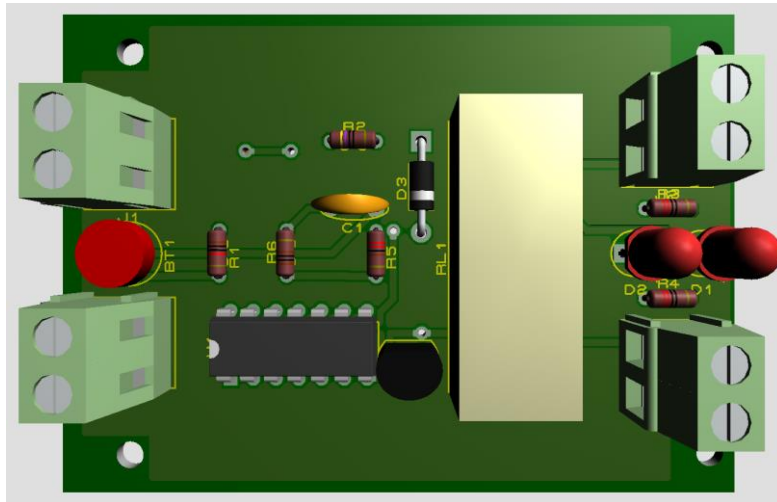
Mặt dưới PCB mạch ứng dụng IC 74LS74.
